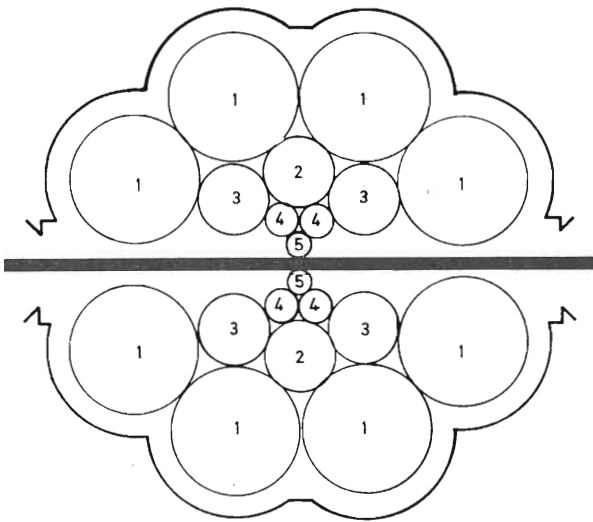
Disposizione dei cilindri in un laminatoio di tipo Sendzimir a 20 cilindri.
